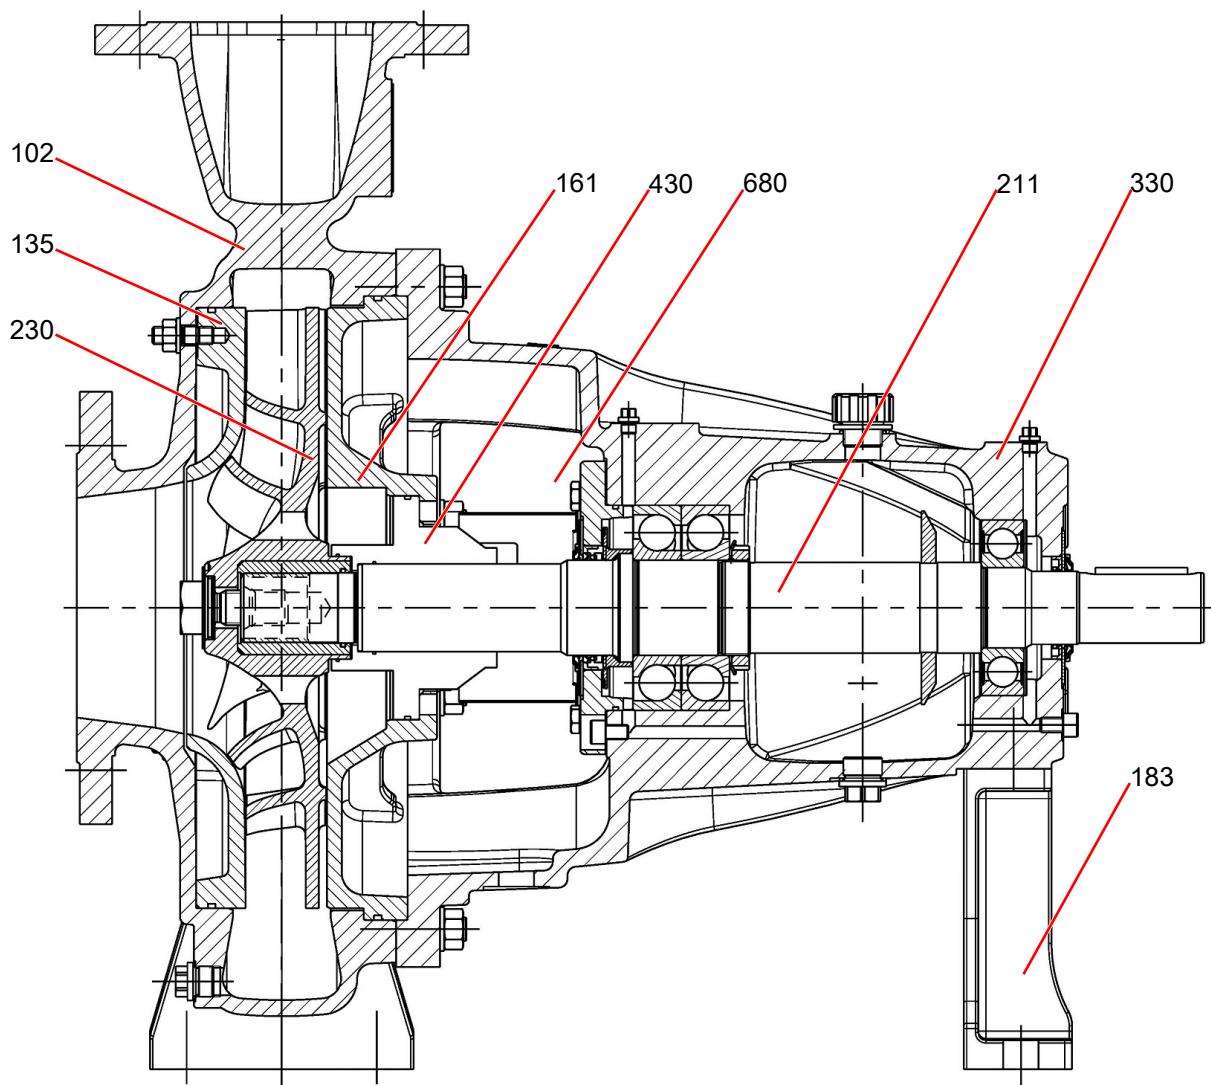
Центробежный насос ACP — основной разрез (полуоткрытое рабочее колесо)
